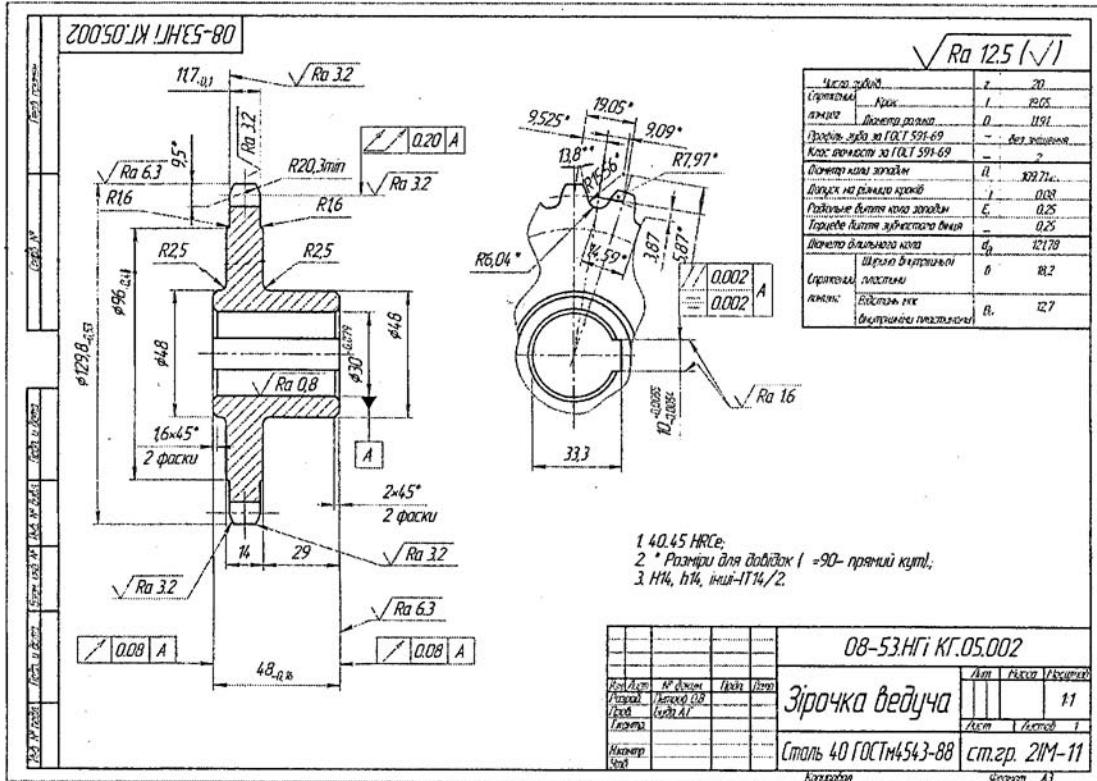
Робочий кресленик ведучої зірочки з пластинчасто-роликовим ланцюгом
